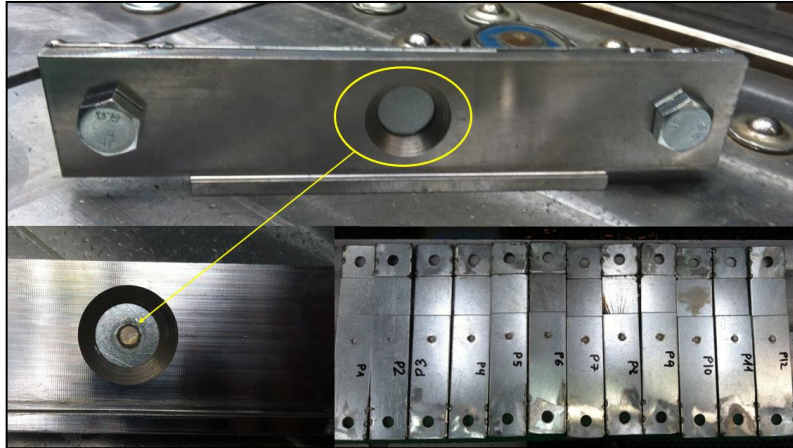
Pinzas de la máquina de soldar por puntos y cabezal de cobre para soldeo por resistencia.
